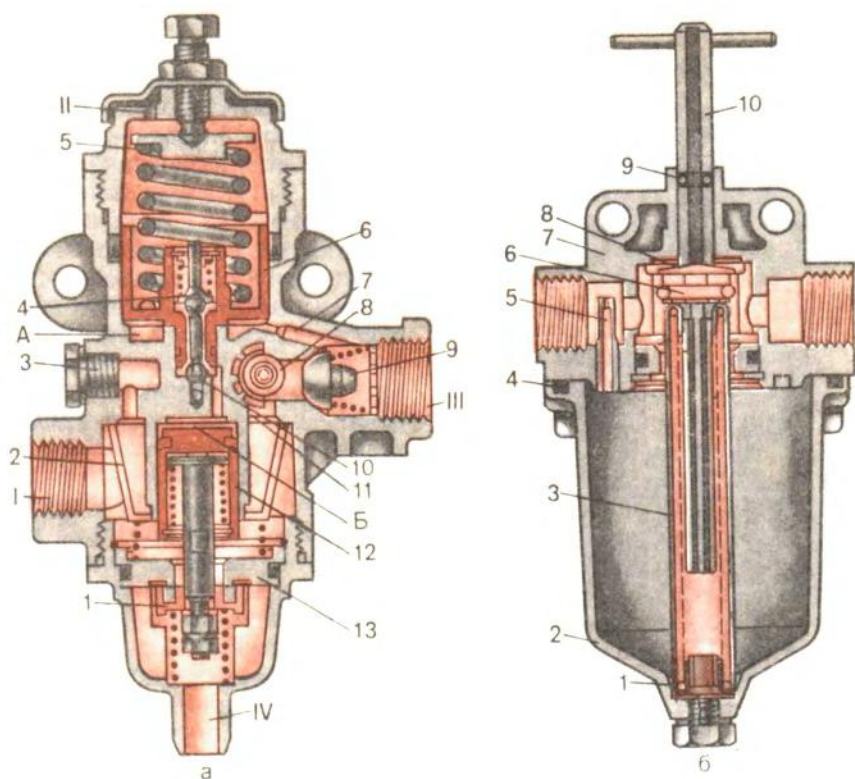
Сборочные единицы пневмопривода автомобилей КамАЗ:
